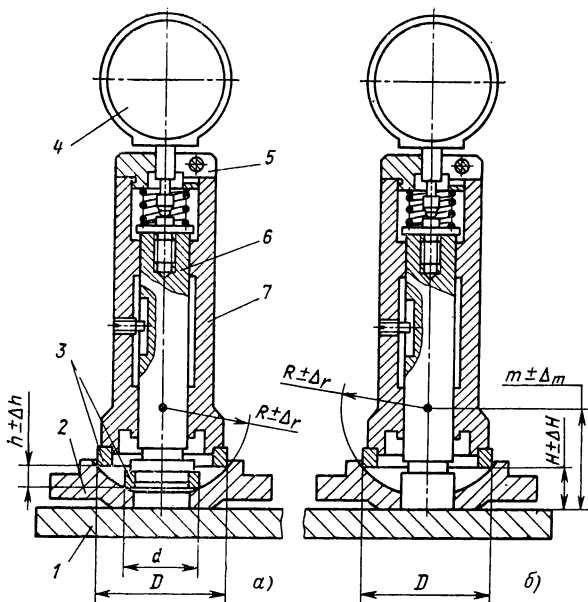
Сферометры для контроля радиуса (а) и положения центра (б) сферических поверхностей
